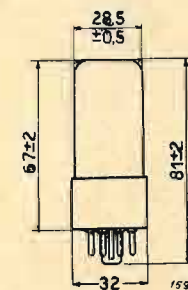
Dimensioni d'ingombro della valvola 6E5GT.
